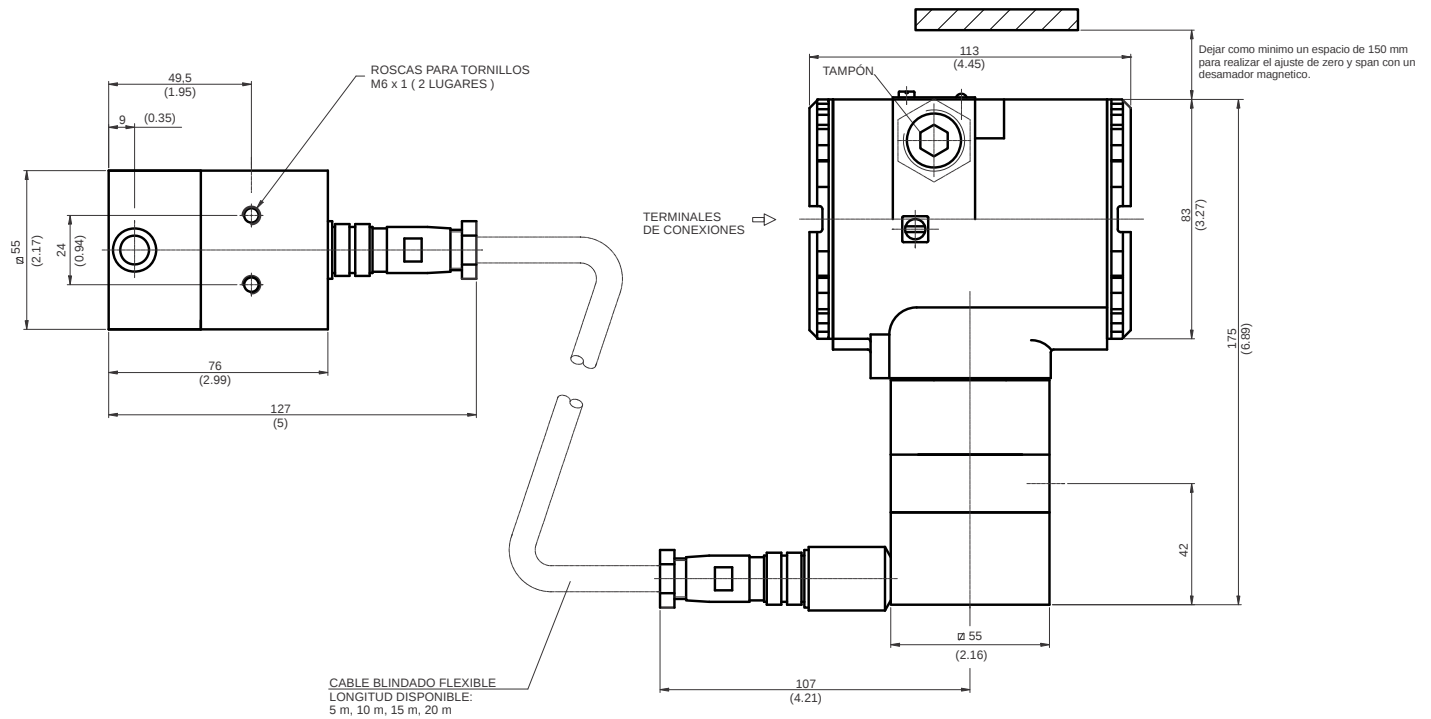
Dibujo Dimensional del TP301 / Dibujo Dimensional de los Imanes / Sensor Remoto
